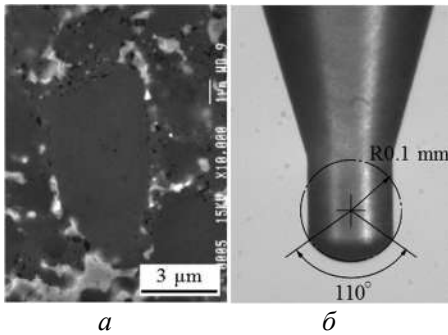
Стан поверхні (а) інструмента з PCD (б) для мікрошліфування [46].
